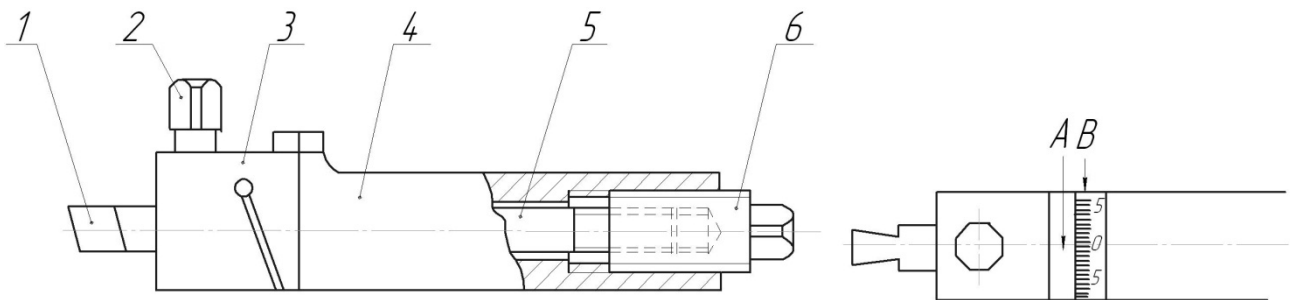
Державка с поворотной головкой для резьбового резца: 1 - резец; 2 - крепежный винт; 3 - поворотная головка; 4 - корпус; 5 - затяжной шток; 6 - гайка - винт; А - риска на головке; В - шкала на корпусе
